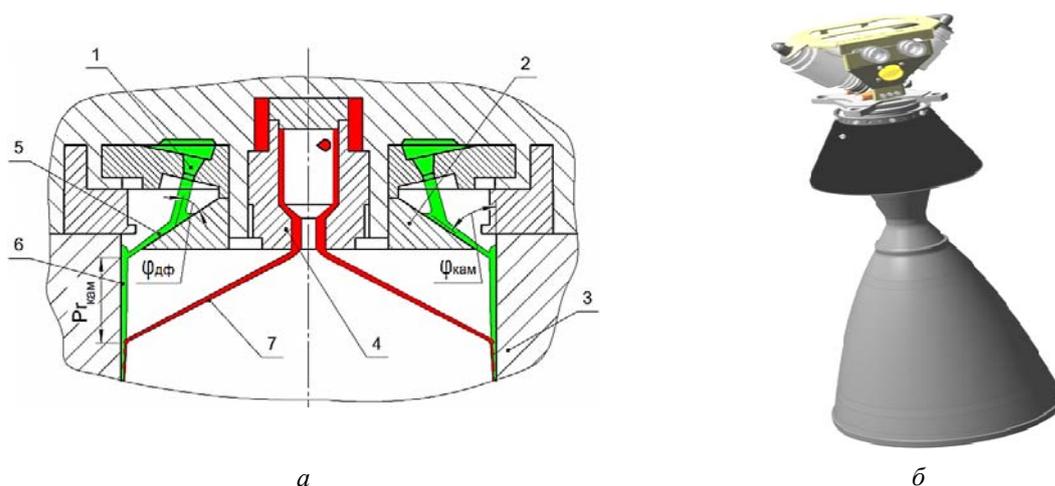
Двухкомпонентный ракетный двигатель малой тяги С5.165:
